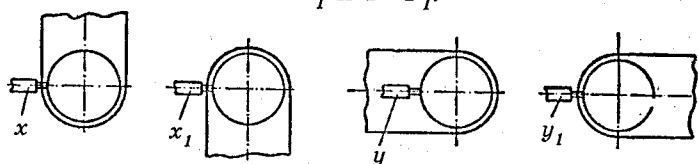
Установка шатунной шейки коленчатого вала при шлифовке
